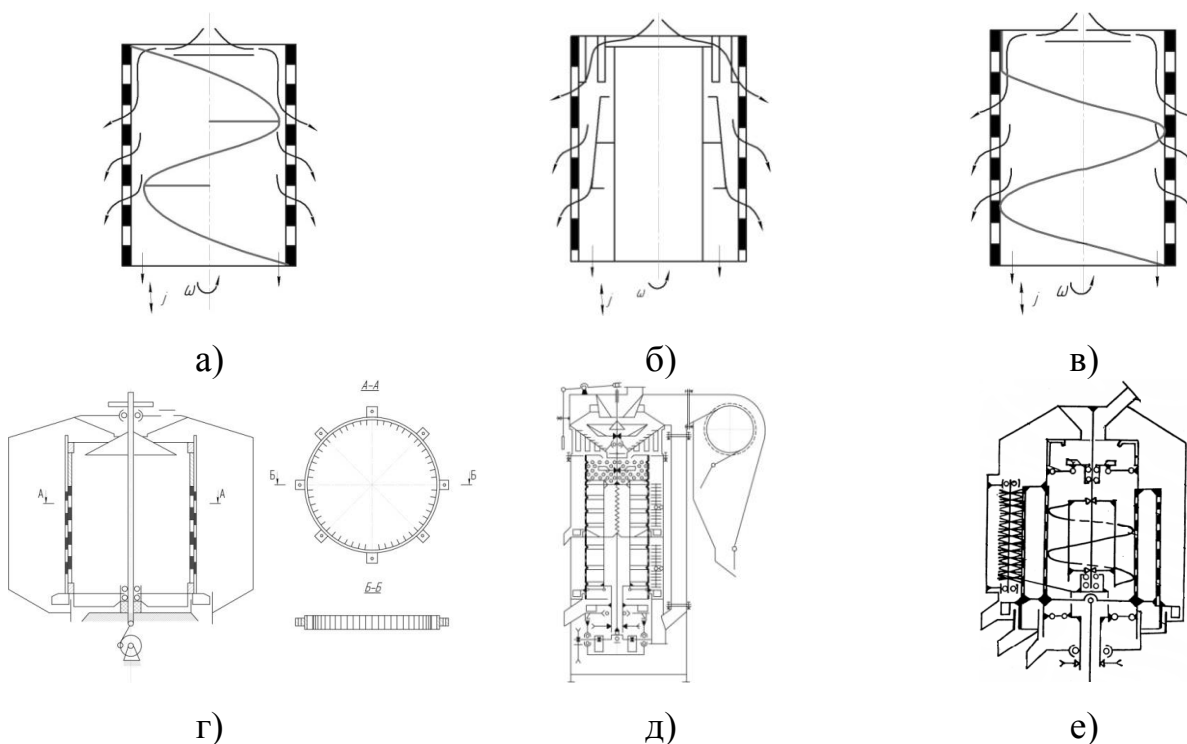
Устройства для стабилизации зернового материала в верхней части цилиндрического решета
